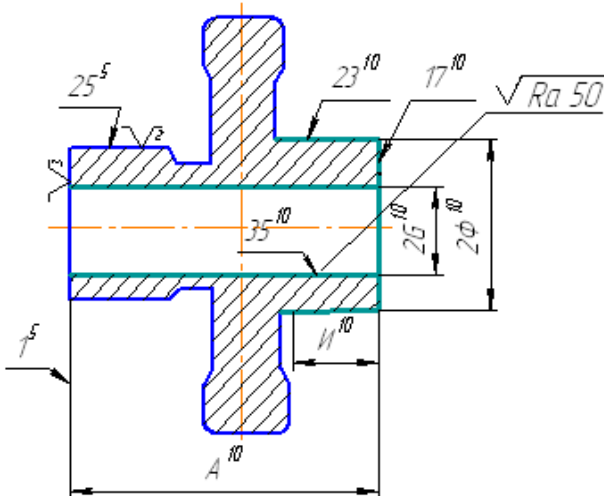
Преобразованный чертеж детали на ось OZ
